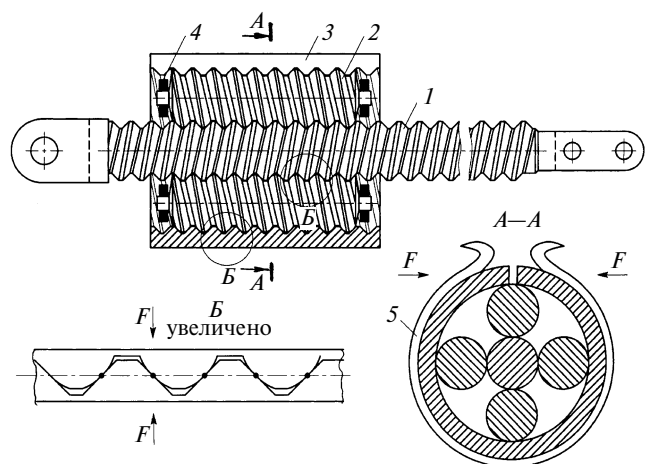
Передача винт—гайка с треугольным профилем резьбы:
